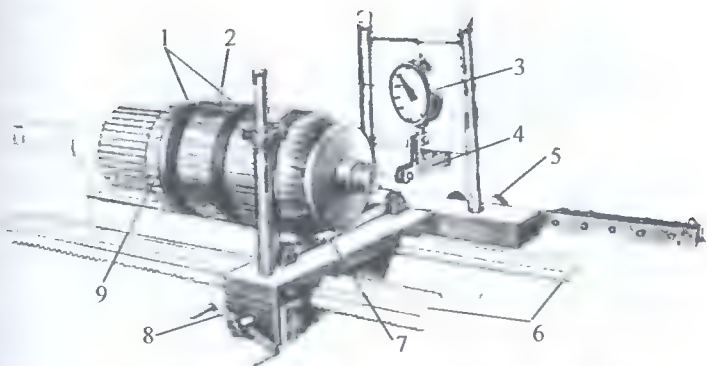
Токарный станок с приспособлением для наложения бандаж: 1 — бандаж; 2 — кольцевая канавка пазовой части обмотки; 3 — динамометр; 4 — подвижный ролик; 5 — натяжное устройство; 6 — параллели токарного станка; 7 — бандажная проволока; 8 — каретка; 9 — ротор
